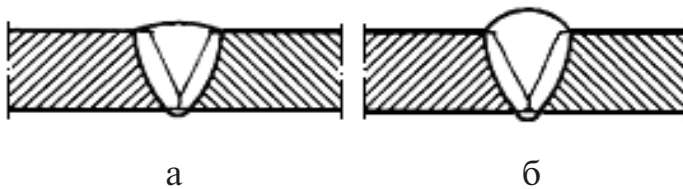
Схематичное изображение превышения усиления сварного шва:
